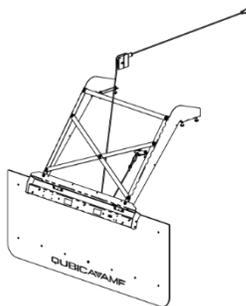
, Schild/Beleuchtung-Baugruppe
